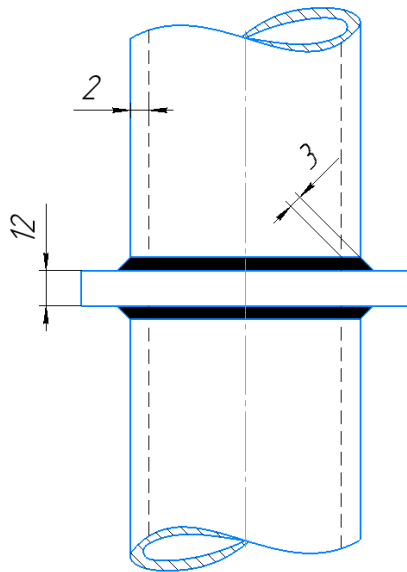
Схема хрестоподібного зразка для випробування труб
